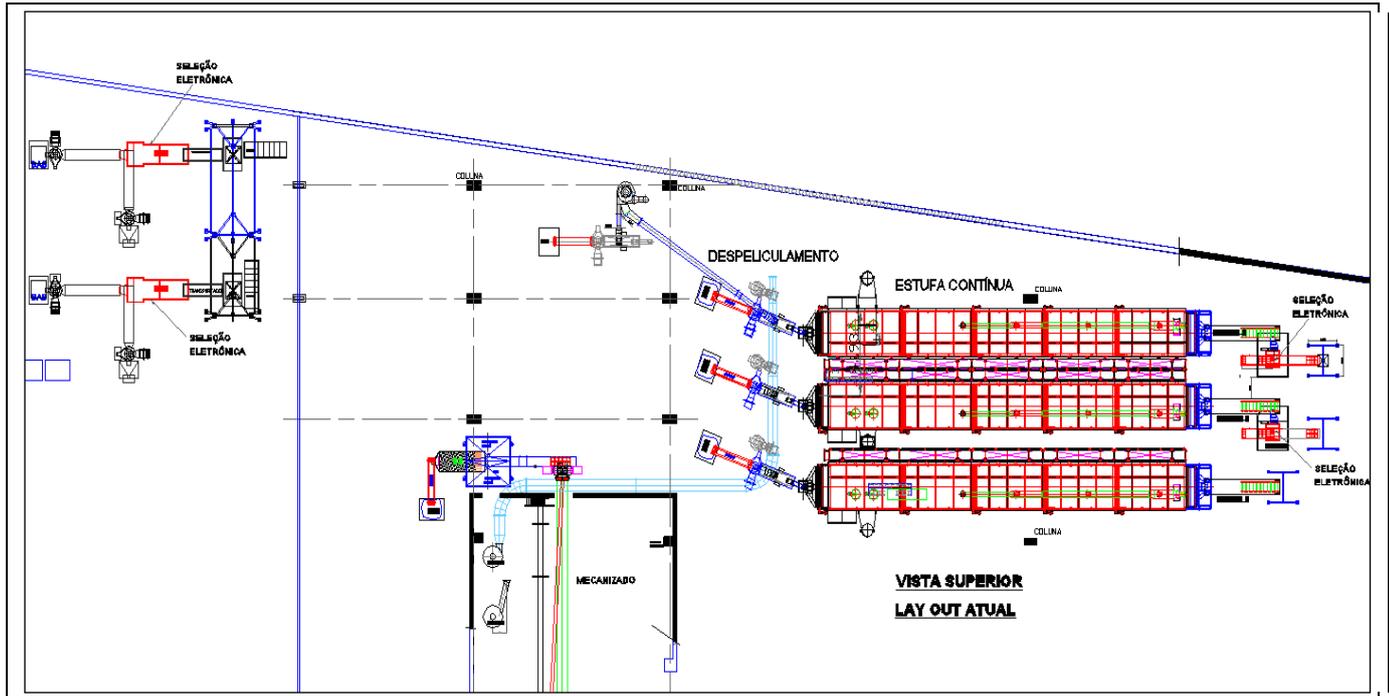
Planta baixa do layout atual do setor mecanizado e produção da Fábrica 3
